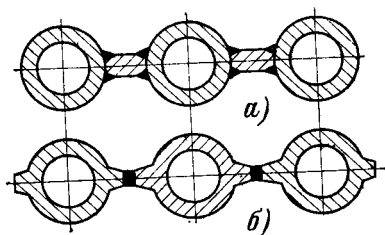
Конструкции сопряжения труб цельносварной панели.
